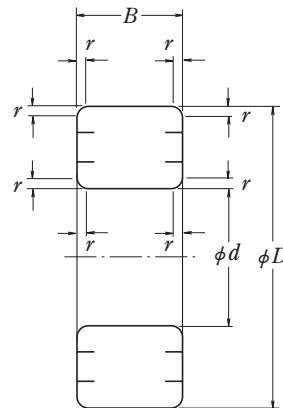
Äußere Abmessungen für Radialkugel- und rollenlager
